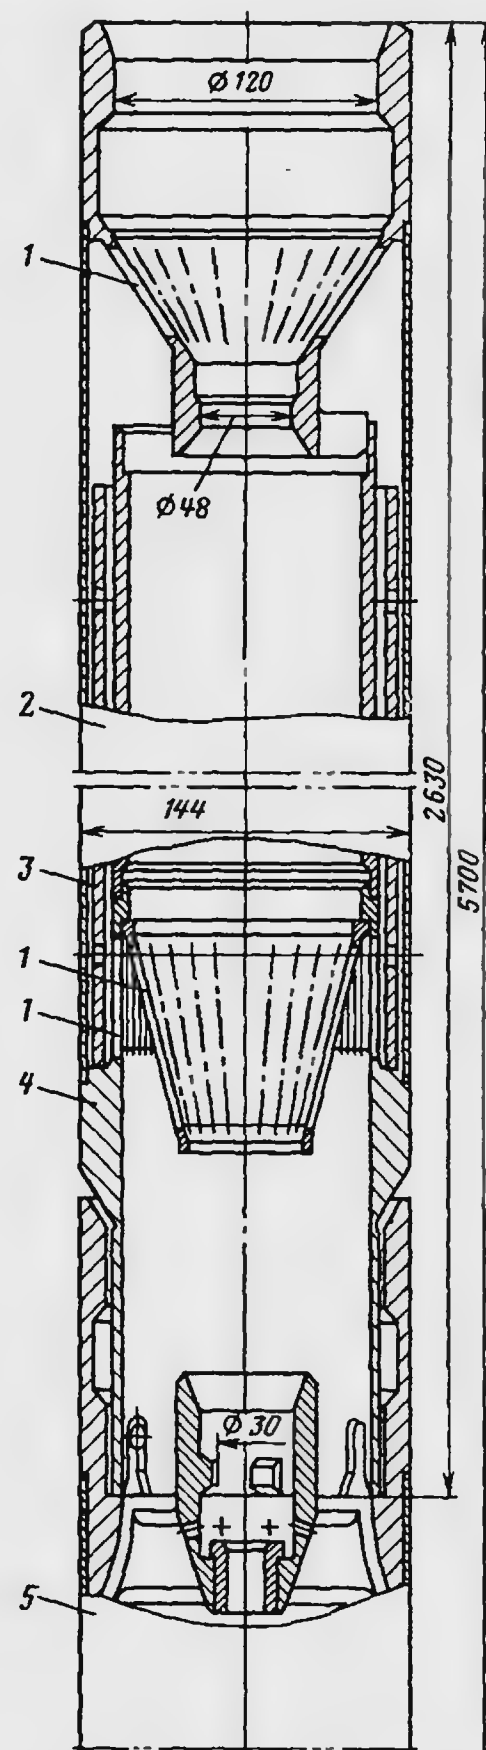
Поглощающая надставка регулирующей сборки:
